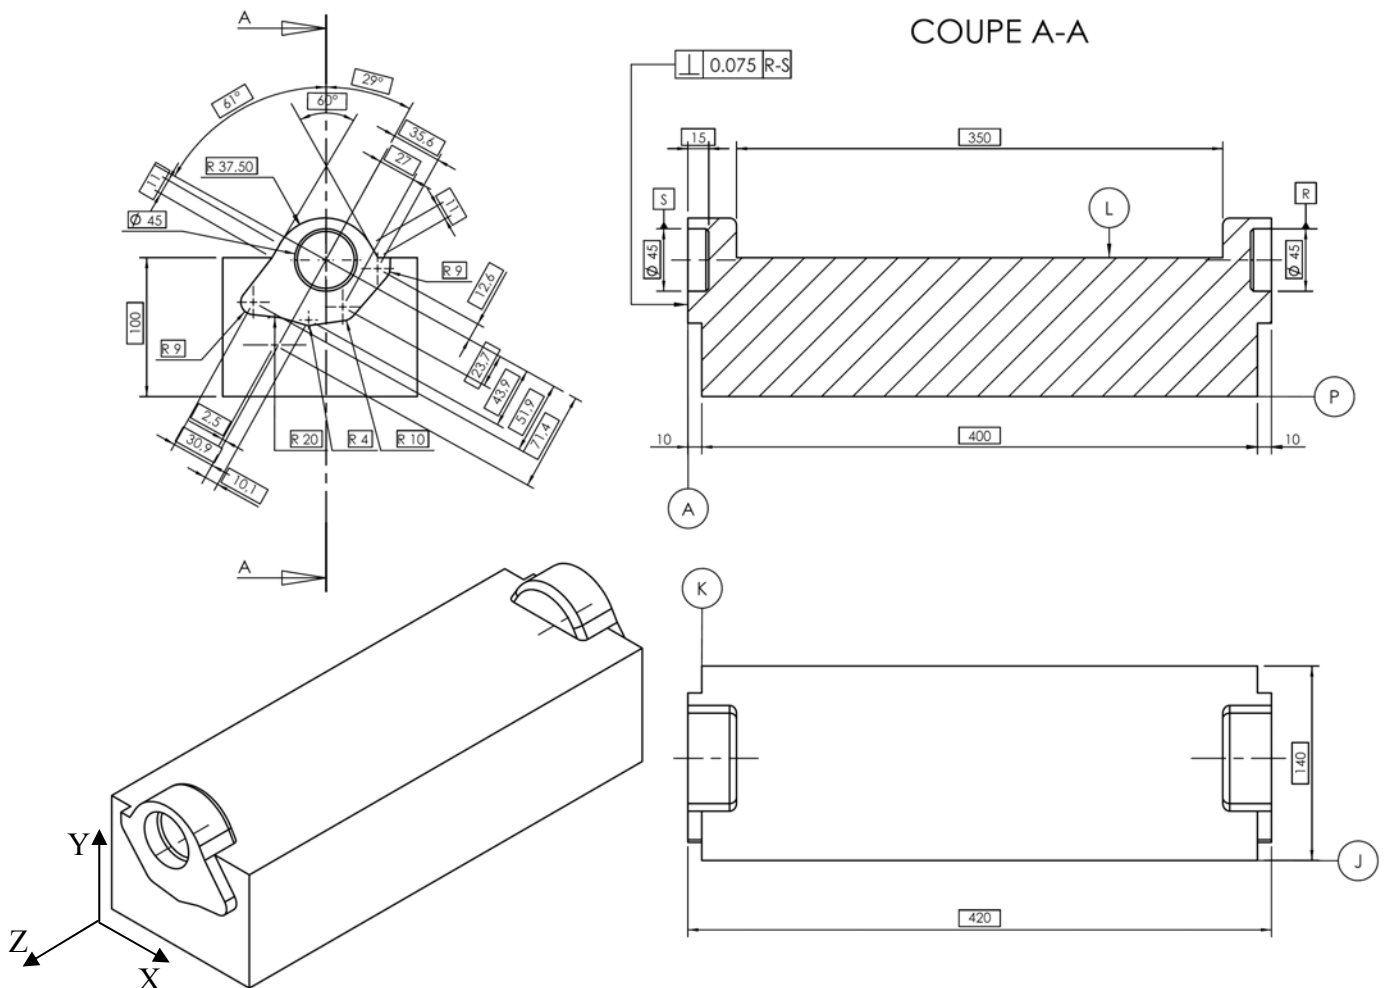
Vue isométrique et dessin de définition simplifiés.
